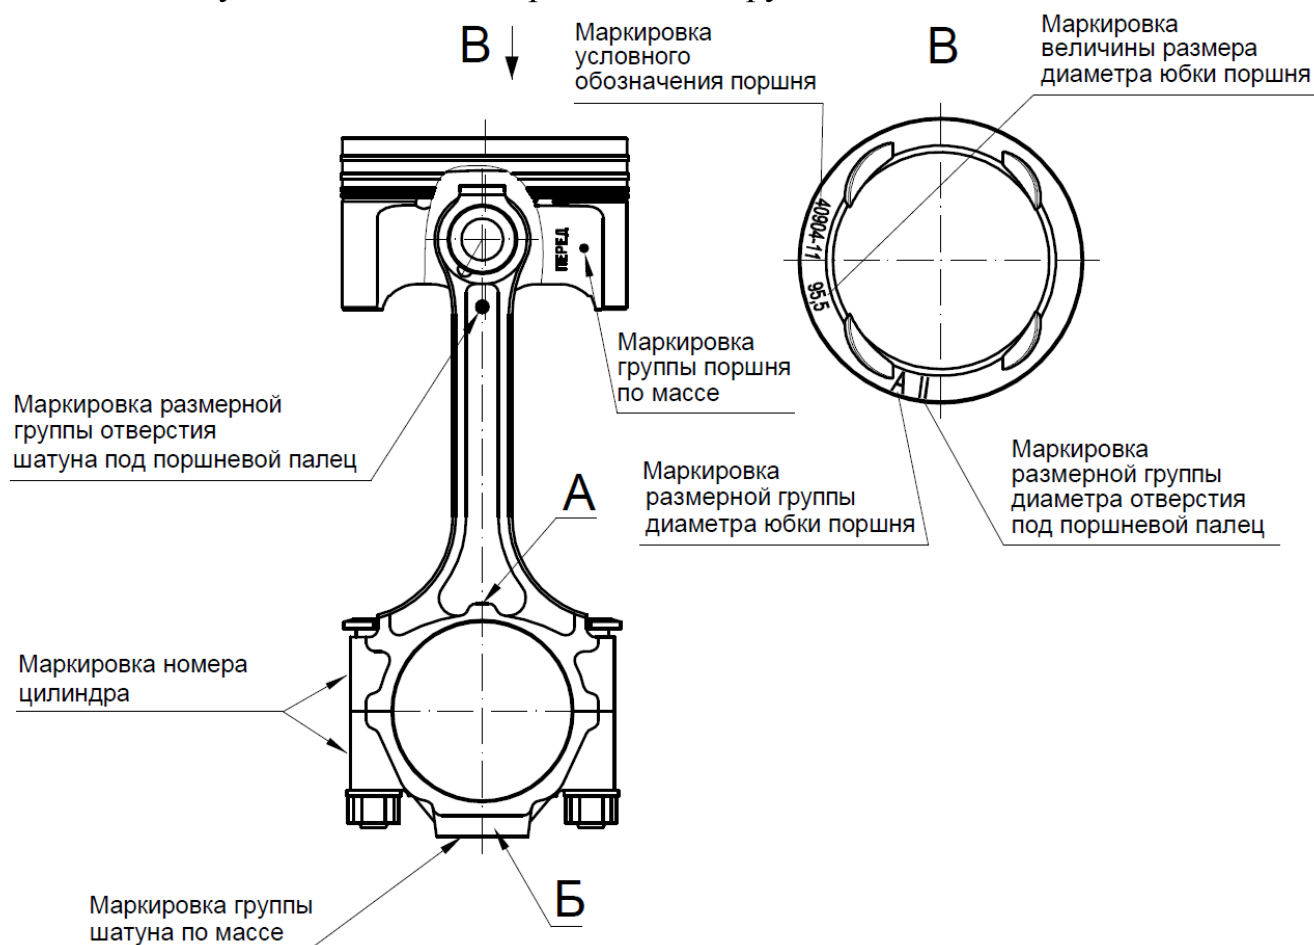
Маркировка шатуна 406.1004045-01 и поршня
